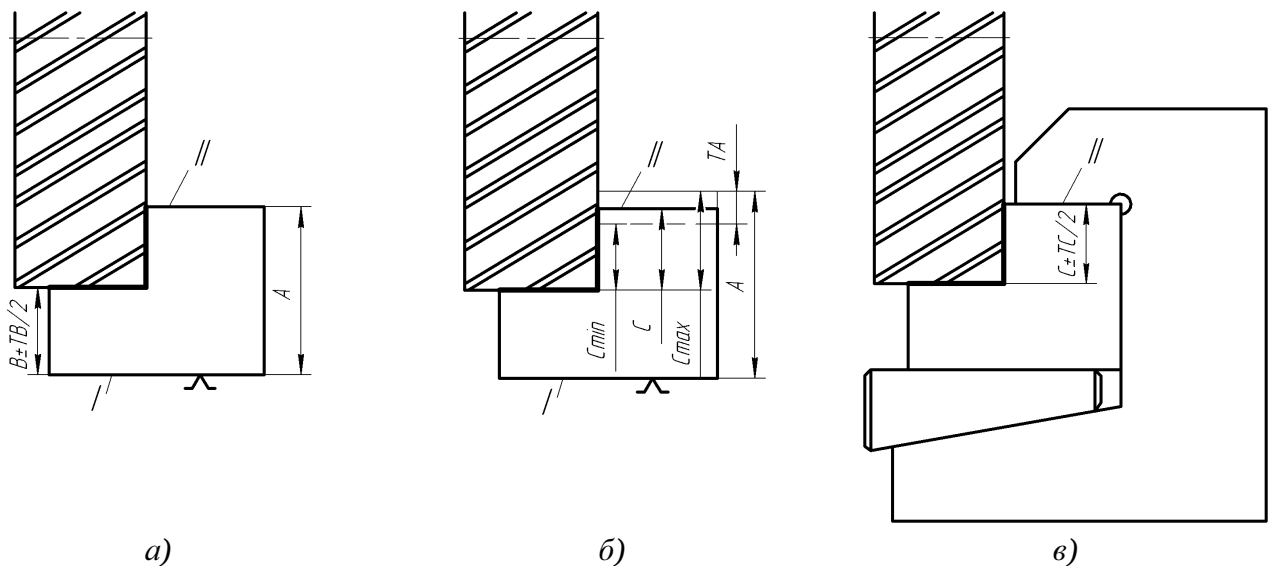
Визначення похибки базування при встановленні заготовки на плоскі поверхні
